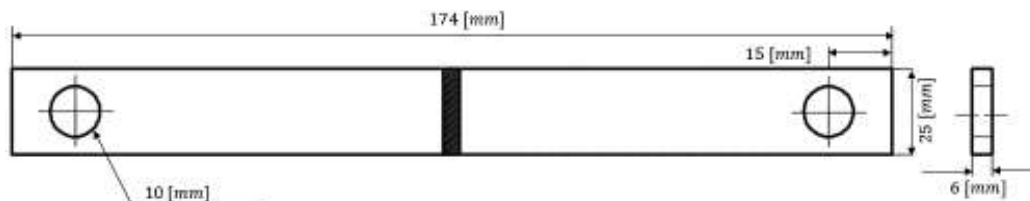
Dimensiones de probetas para ensayo de corrosión.
